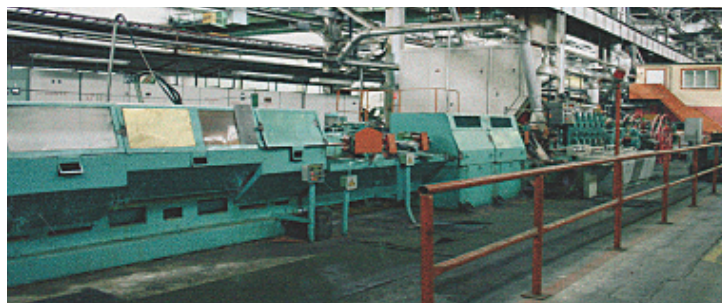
Трубосварочный агрегат ТЭСА 15-50
